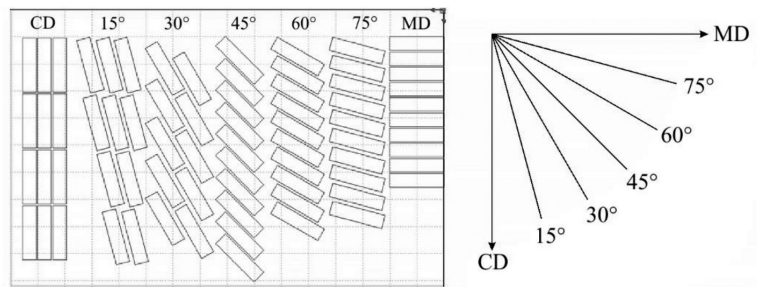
Рабочий эскиз для лазерной резки элементов изделий с различным углом расположения линий склейки гофров
